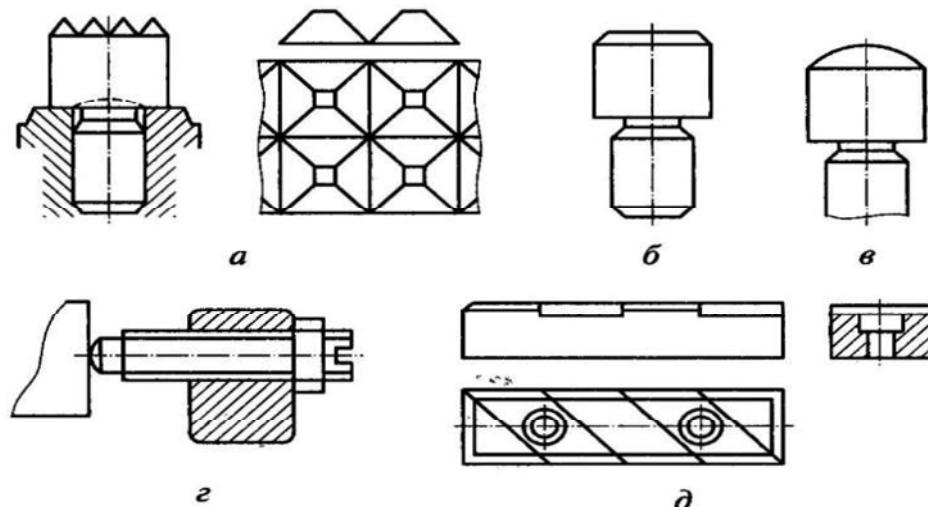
Опоры для установки деталей на плоские поверхности: *а* — с рифленой головкой; *б* — с плоской головкой; *в* — со сферической головкой; *г* — регулируемые; *д* — опорные пластины
